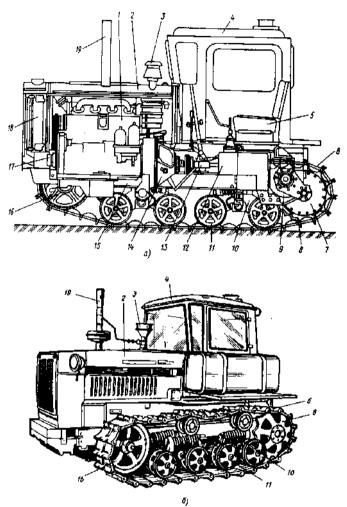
Гусеничный трактор типа ДТ-75НР; а – компоновочная схема сборочных единиц; б – общий вид; 1 – двигатель; 2 – капот двигателя; 3 – воздухозаборник; 4 – кабина; 5 – рабочее место машиниста; 6 – цепь; 7 – редуктор; 8 – звездочка; 9 – задний мост; 10 – эластично-балансирная каретка; 11 – каток; 12 – коробка передач; 13 – вал; 14 – муфта сцепления; 15 – рама; 16 – направляющее колесо; 17 – гидронасос; 18 – радиатор; 19 – выхлопная труба
